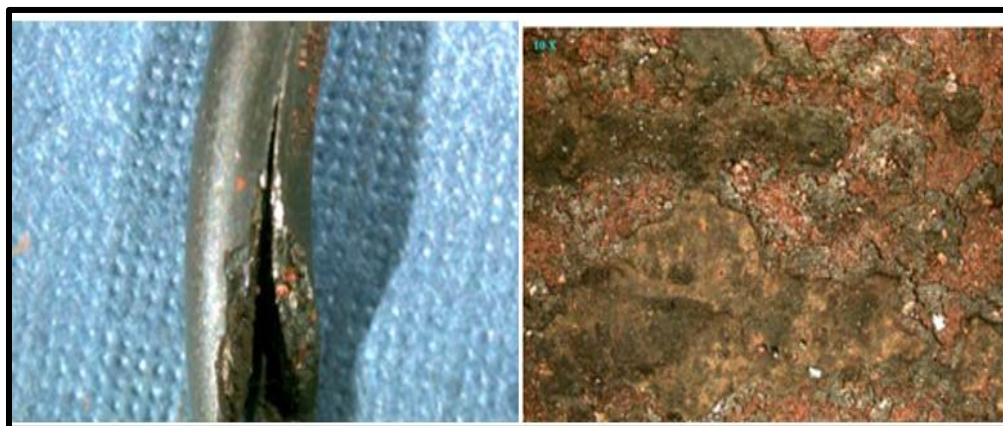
Fisuración y agrietamiento (Izquierda) y generación de sulfuro de hierro (Derecha)
